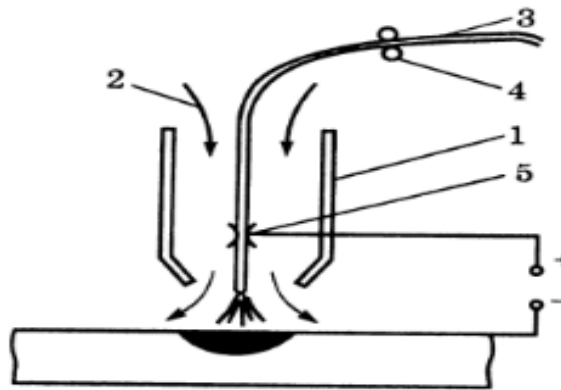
Схема процесу зварювання в захисних газах електродом, що плавляється: 1 – сопло зварювального пальника; 2 – подача захисного газу; 3 – зварювальний дріт; 4 – ролики, що подають; 5 – струмопровід
